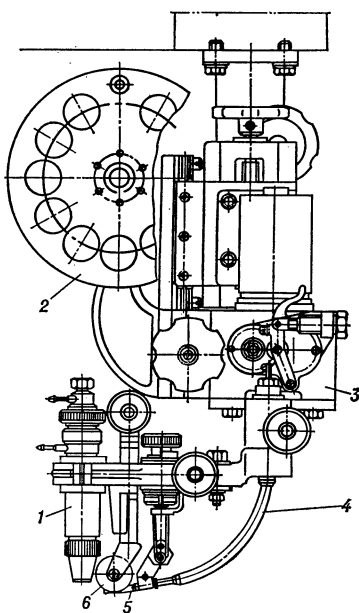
Сварочный полуавтомат для электросварки неплавящимся вольфрамовым электродом с подачей присадочной проволоки: 1 — горелка; 2 — катушка; 3 — механизм подачи; 4 — направляющий шланг; 5 — наконечник; 6 — прижимной ролик.
